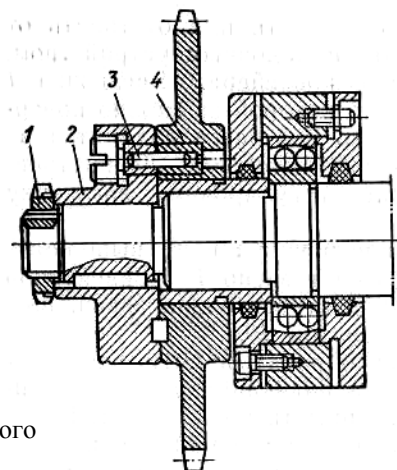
Предохранительное устройство для отключения конвейера шипорезного станка: 1 — гайка, 2 — муфта, 3 — штифт, 4 — звездочка
